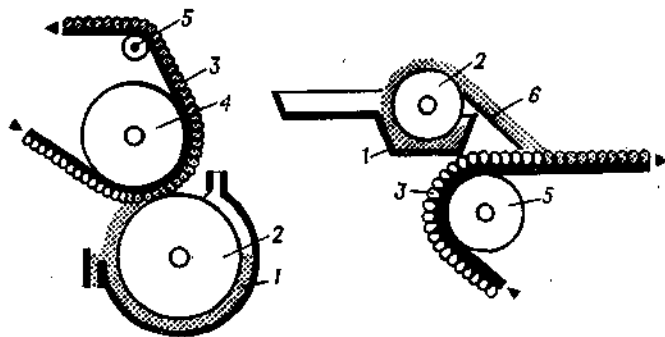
Установка для непрерывного крашения ворсовых ковров:
